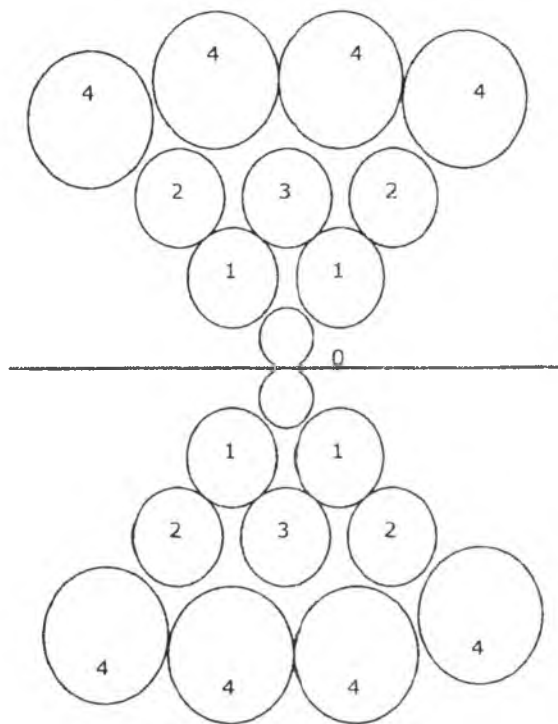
Конструктивный вид валков прокатного стана Сендзимира:
